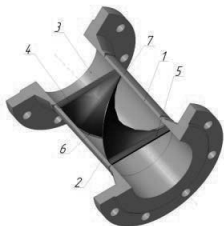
Объемное изображение устройства для очистки трубопровода.
